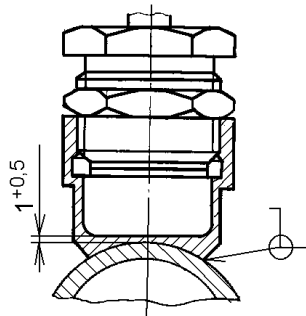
Установка ТСП/1-8044 с основанием ЮВМА.713133.001
